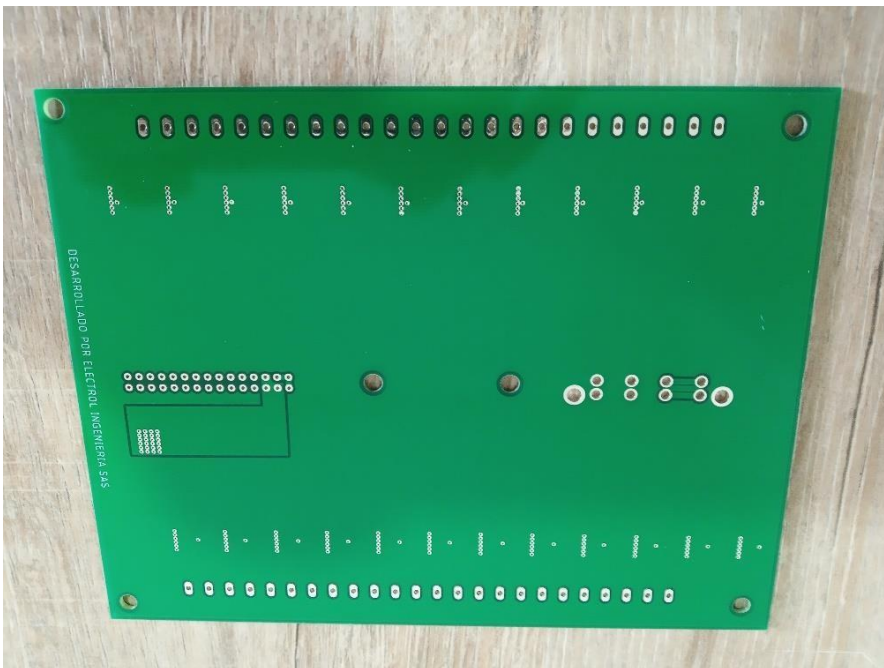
Tarjeta DC PCB secuenciador de luces [Vista inferior]. Tobón. (2019)
